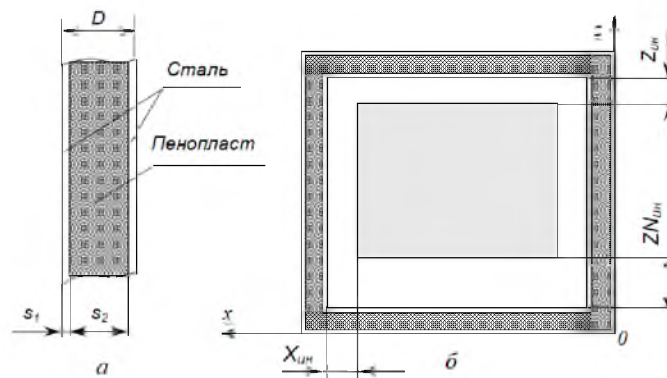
Устройство стенки (а) и разрез корпуса (б)
